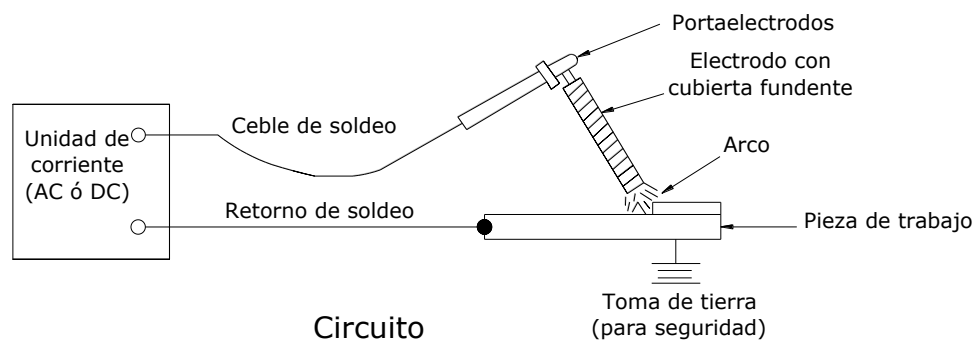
Proceso SMAW (Shielded metal arc welding)
